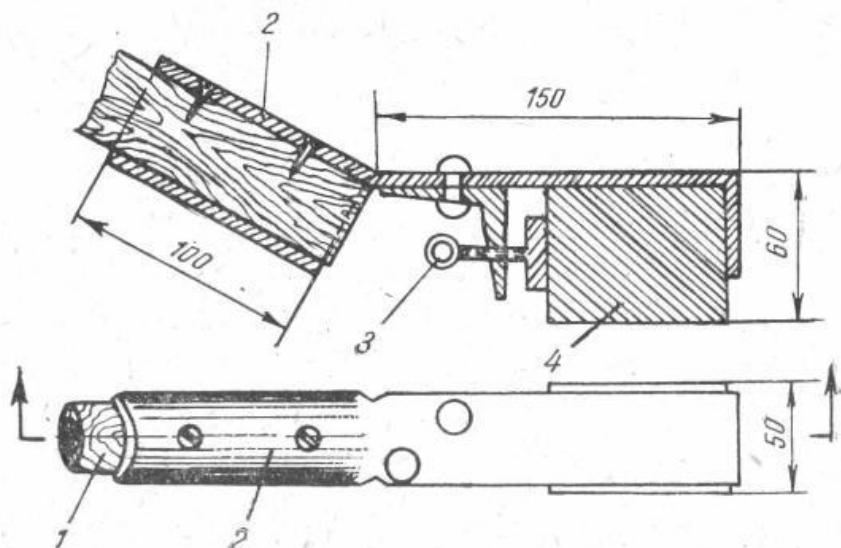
Ramă metalică pentru fixarea pietrei de șlefuit:
